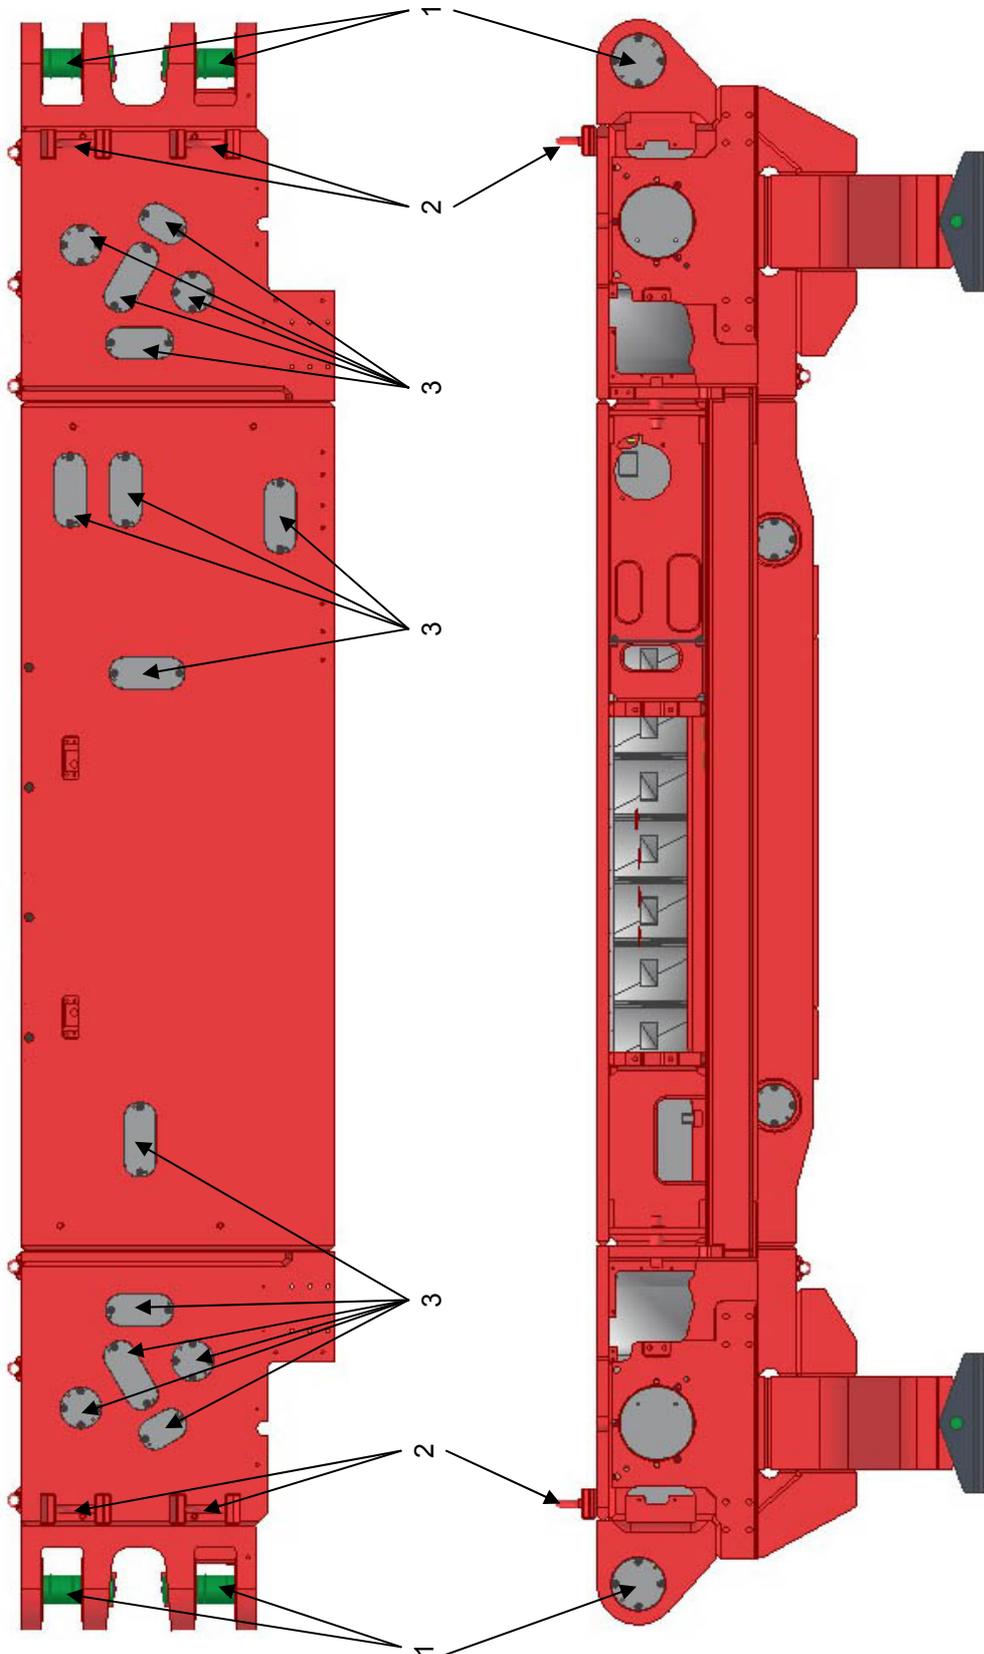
Показывает устройство якорного пальца для домкрата поворотного редуктора.
